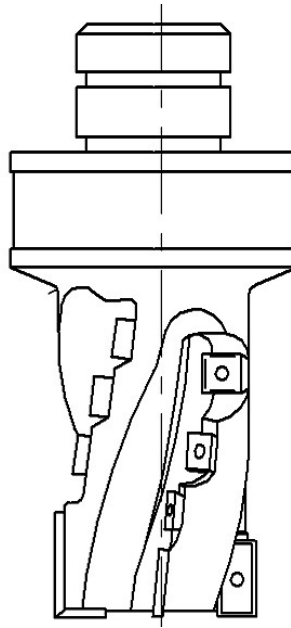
Конструкція фрези гвинтової з механічним кріпленням пластин
